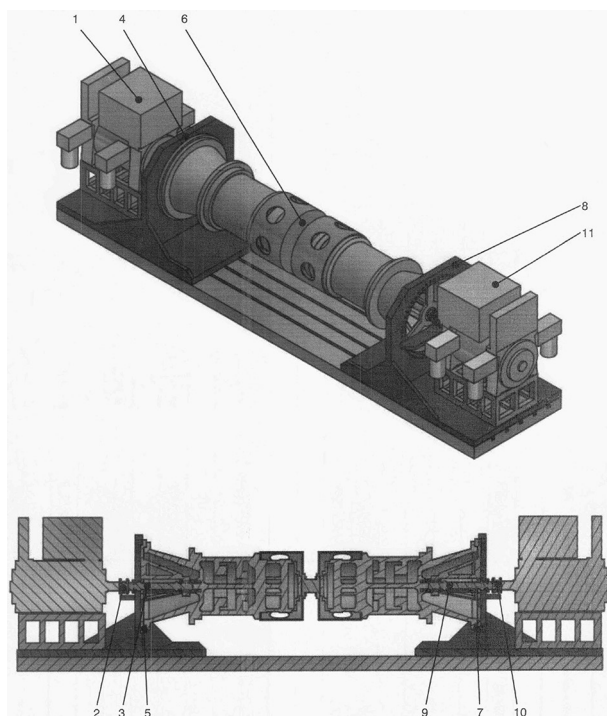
Общая схема стенда для испытаний РМК самосвалов БЕЛАЗ: 1 — приводной электродвигатель (ЭД1); 2 — датчик момента приводного двигателя; 3 — промежуточный вал с оснасткой приводного двигателя (комплект); 4 — опорный кронштейн 1-го испытуемого редуктора (РМК1) с опорной конструкцией приводного двигателя; 5 — переходной фланец (комплект); 6 — соединительный вал с переходными фланцами (комплект); 7 — переходной фланец (комплект); 8 — опорный кронштейн 2-го испытуемого редуктора (РМК2) с опорной конструкцией нагружающего двигателя; 9 — промежуточный вал с оснасткой нагружающего двигателя; 10 — датчик момента нагружающего двигателя; 11 — нагружающий электродвигатель (ЭД2)
